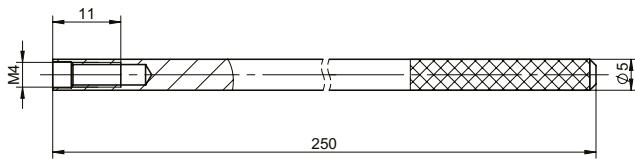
Ausziehwerkzeug Typ 1319 für Blindsensor Typ 6442
